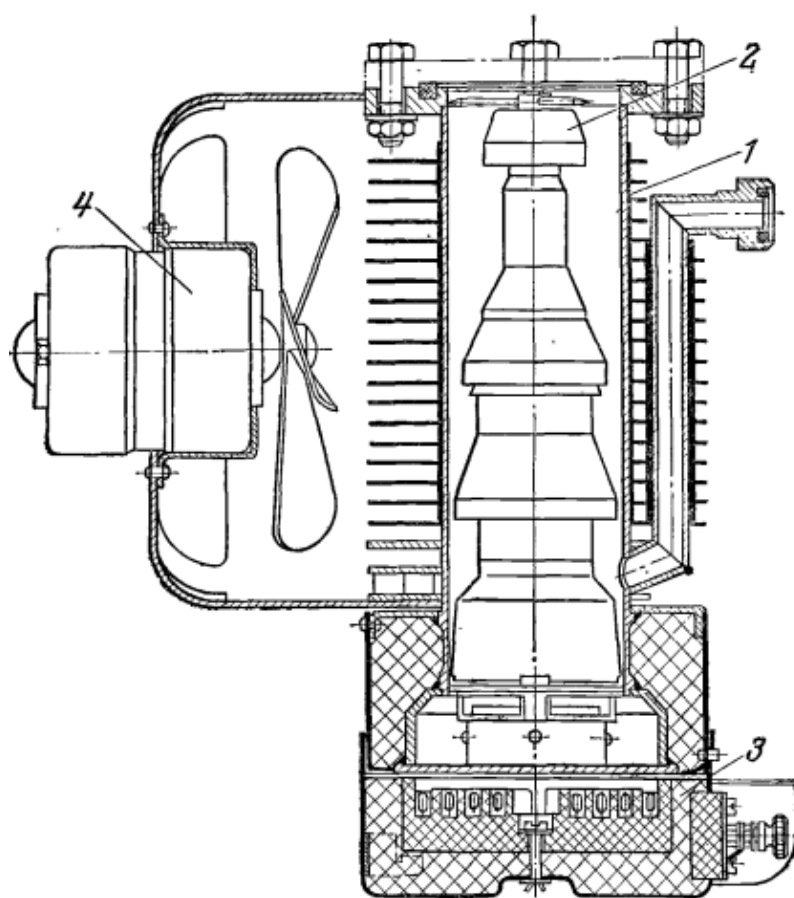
Паромасляный насос НВД-40 с воздушным охлаждением. 1 – ребристый корпус; 2 – паропровод; 3 – нагреватель; 4 – вентилятор [8, с. 140]
